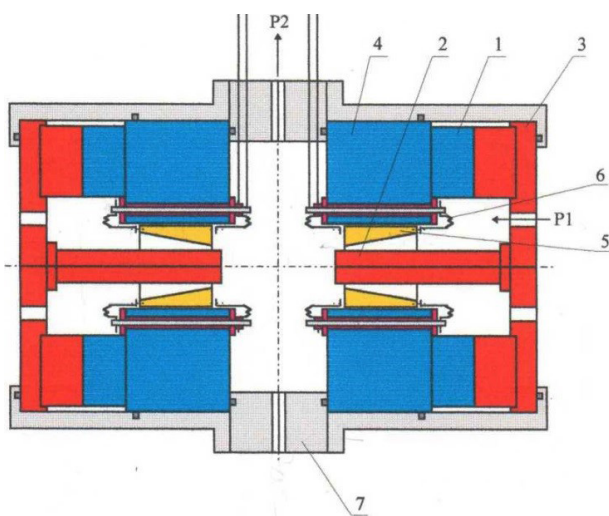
Схема одноступенчатого волнового компрессора симметричной конструкции
